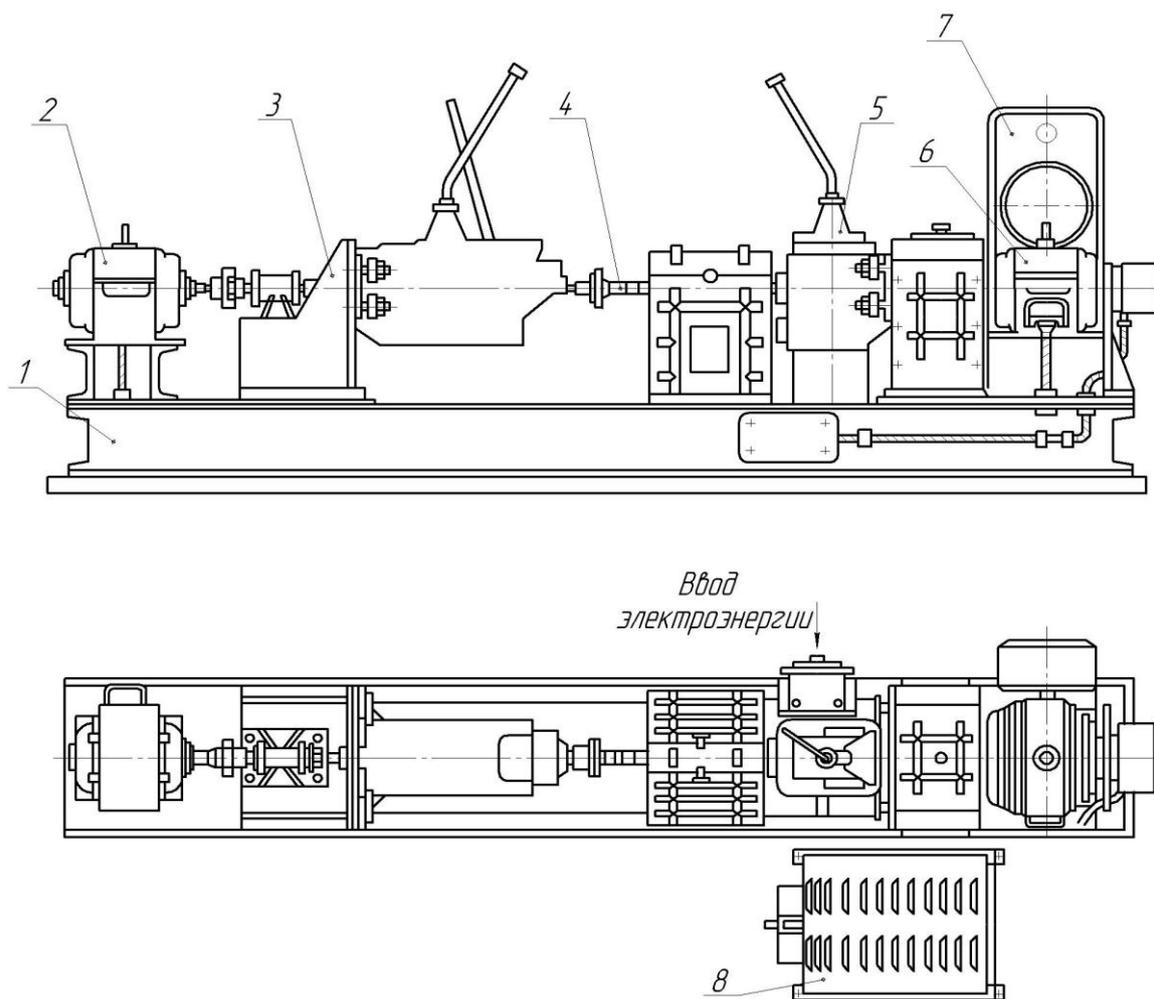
Стенд для испытания коробок передач, модель 5027
